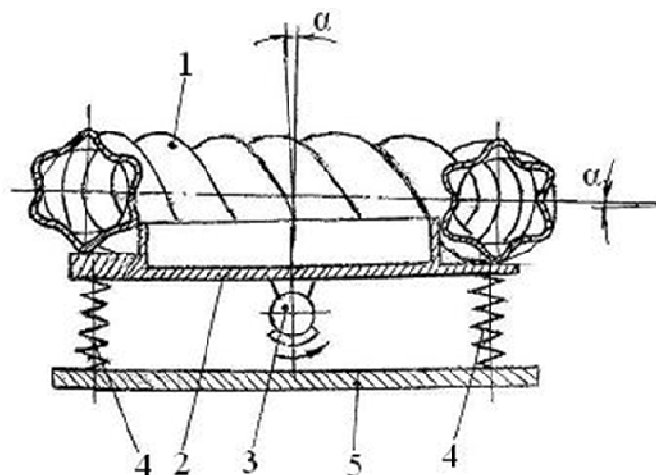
Устройство вибрационное для приготовления кормов, вид спереди
